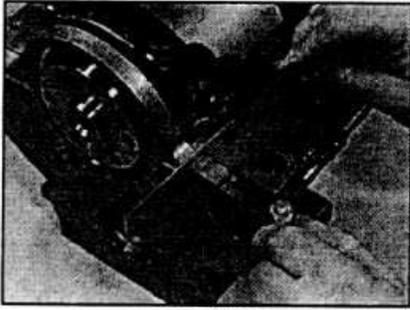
С.63. Проверка установки поверхности крышки левого уплотнительного кольца коленчатого вала, сопрягаемой с масляным поддоном.
